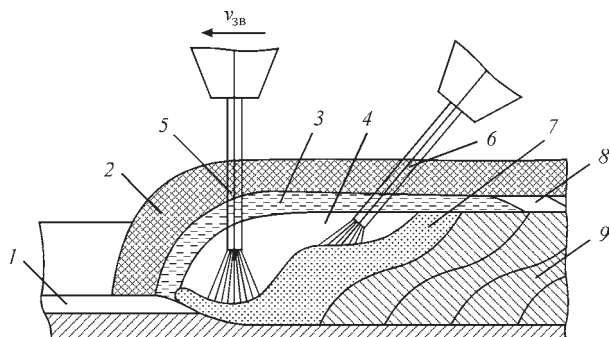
Схема двухдугового зварювання під флюсом із застосуванням модифікованої лігатури [31]: 1 – лігатура; 2 – флюс; 3 – рідкий шлак; 4 – газовий пазир; 5, 6 – електродні дроти; 7 – рідка ванна; 8 – застиглий шлак; 9 – метал шва
